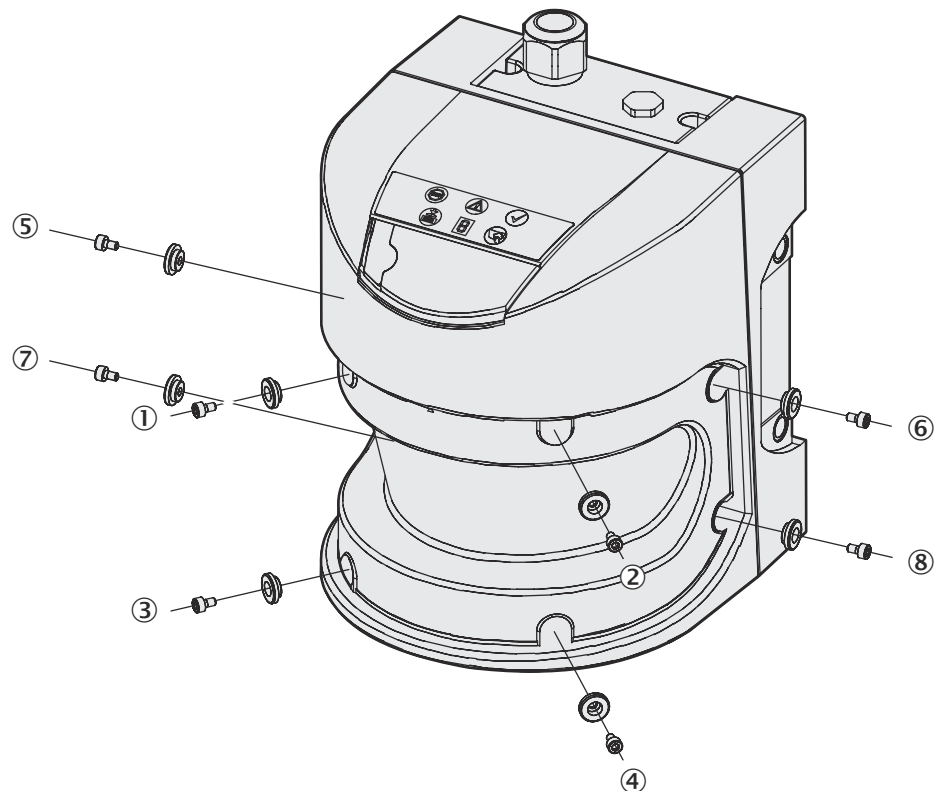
Befestigungsschrauben der Frontscheibe lösen
